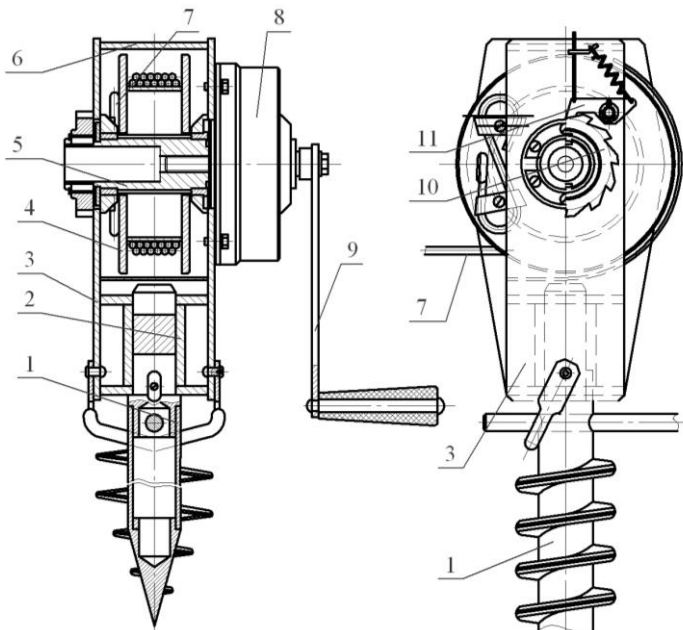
Конструкція підйомно-транспортної гвинтової лебідки: 1 – гвинтова опора; 2 – втулка; 3 – стійка; 4 – приводний барабан; 5 – храпова втулка; 6 – верхня кришка; 7 – канат; 8 – корпус редуктора; 9 – ручка; 10 – храпове колесо; 11 – собачка
